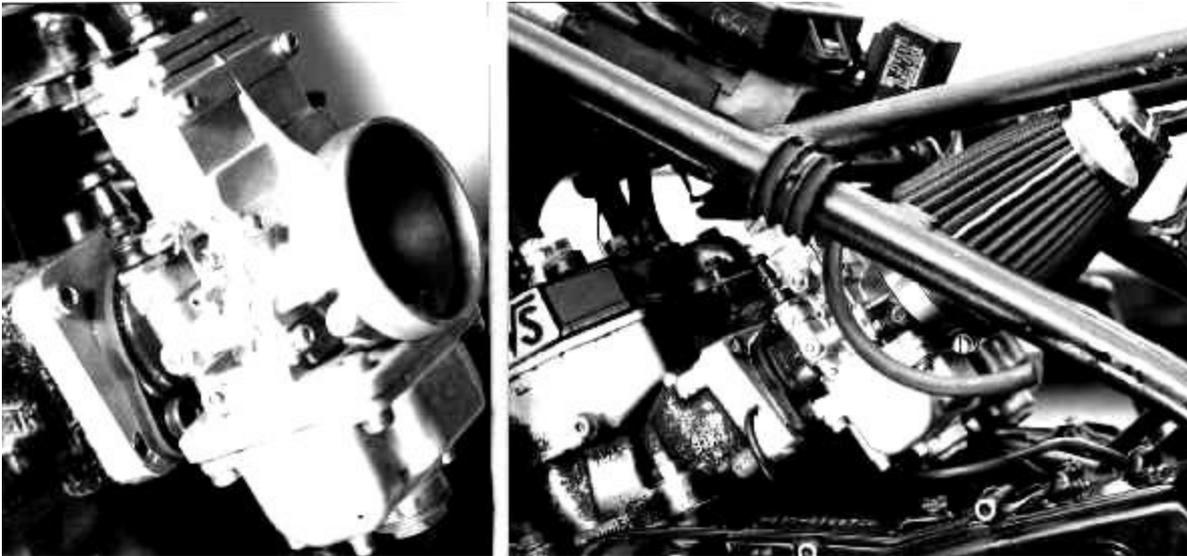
Vergaser TM34 mit Adapterplatte am Zylinder verschraubt
